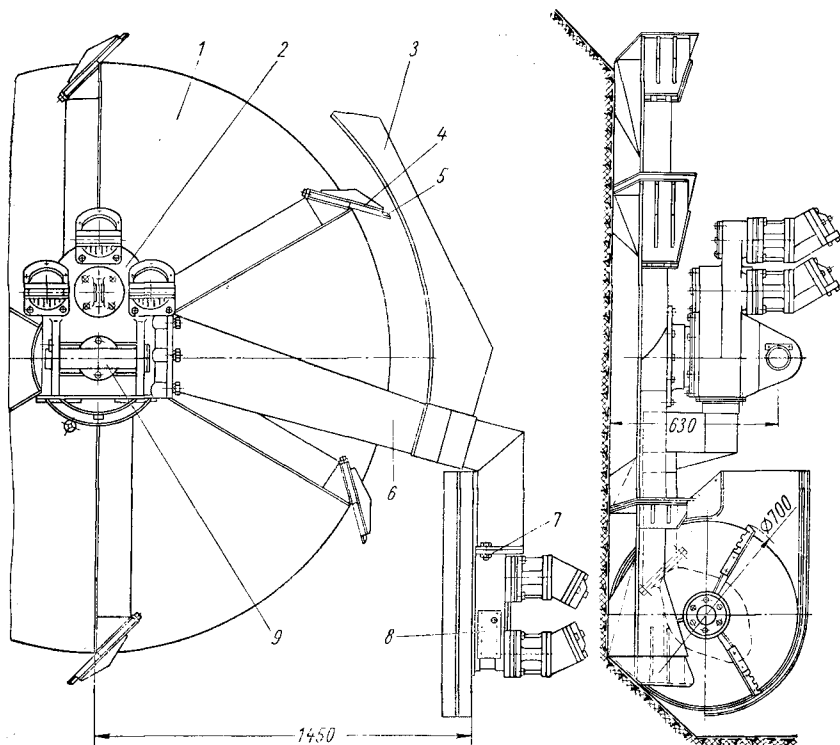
Рабочий орган каналоочистителя КОБ-1.5:
